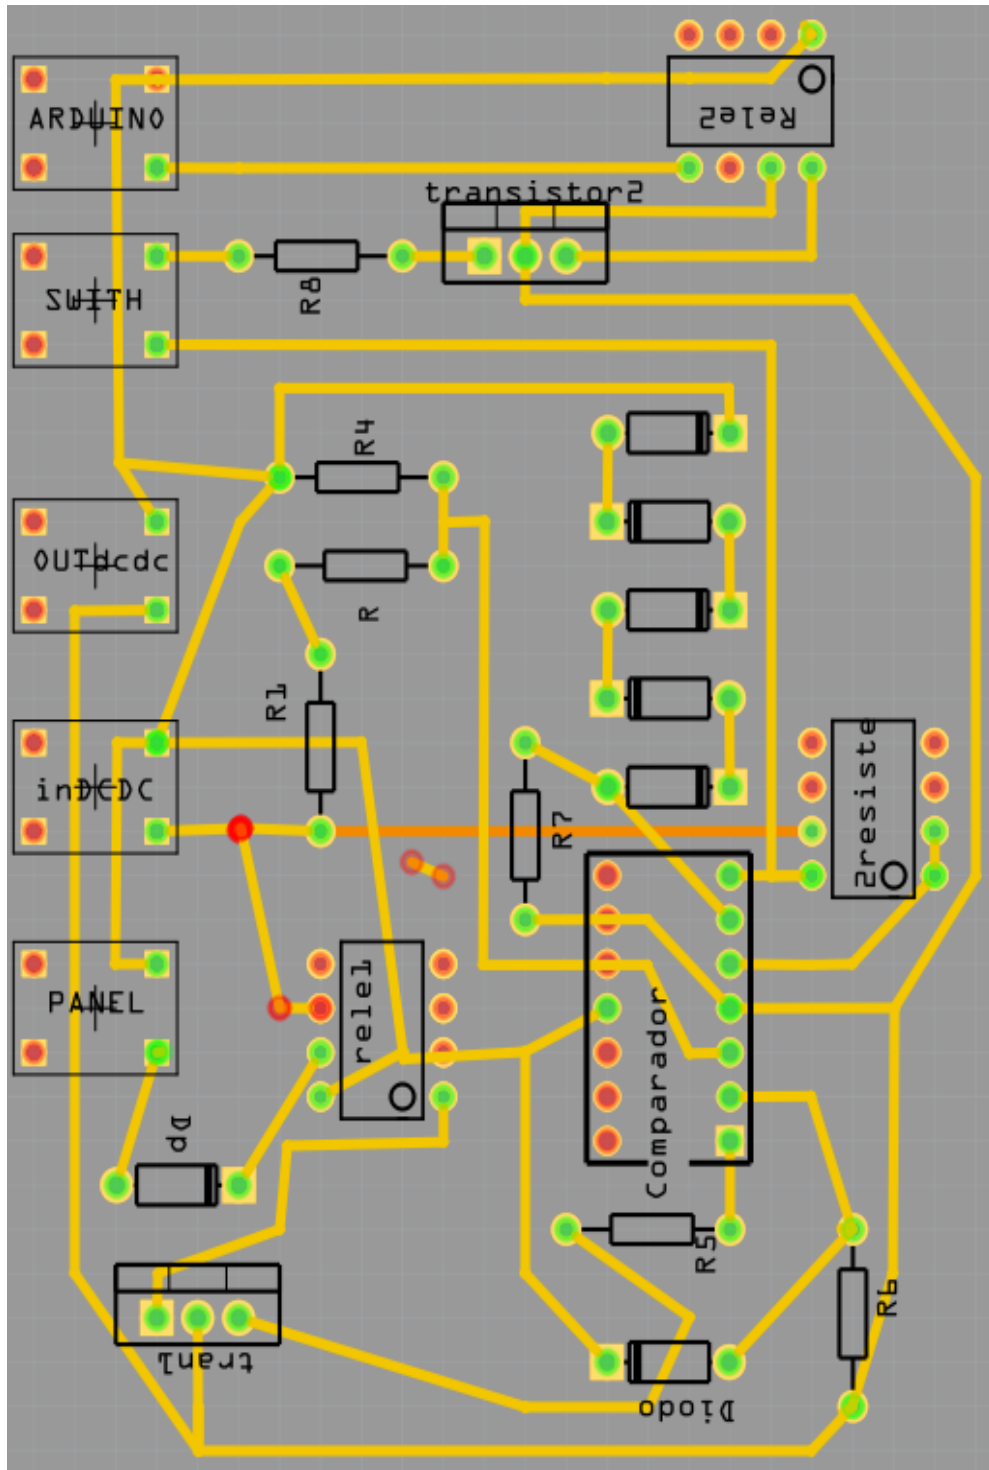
Diseño de la Placa PCB del Circuito de Alimentación en Fritzing Fab
